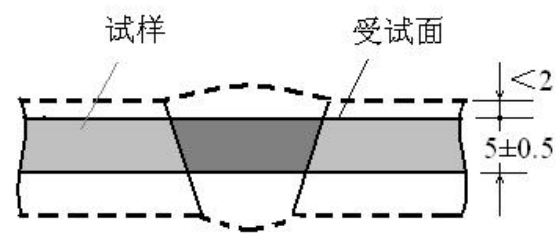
焊接接头试样的取样位置
